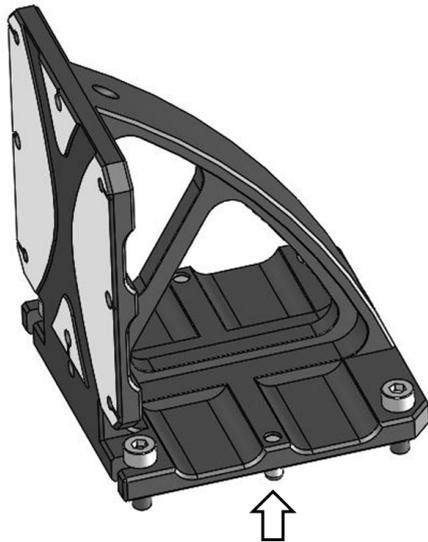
Adapterwinkel mit Schrauben und Passstiften. Die Passstifte für die Ausrichtung auf dem unteren Positionierer müssen von unten bis zum Anschlag in den Winkel eingebracht werden.
